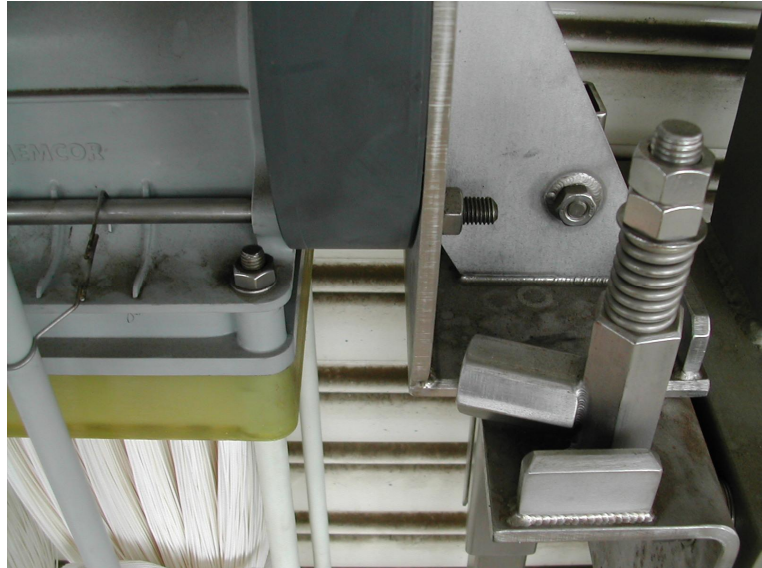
Componenti per il fissaggio del Rack al Supporto.
